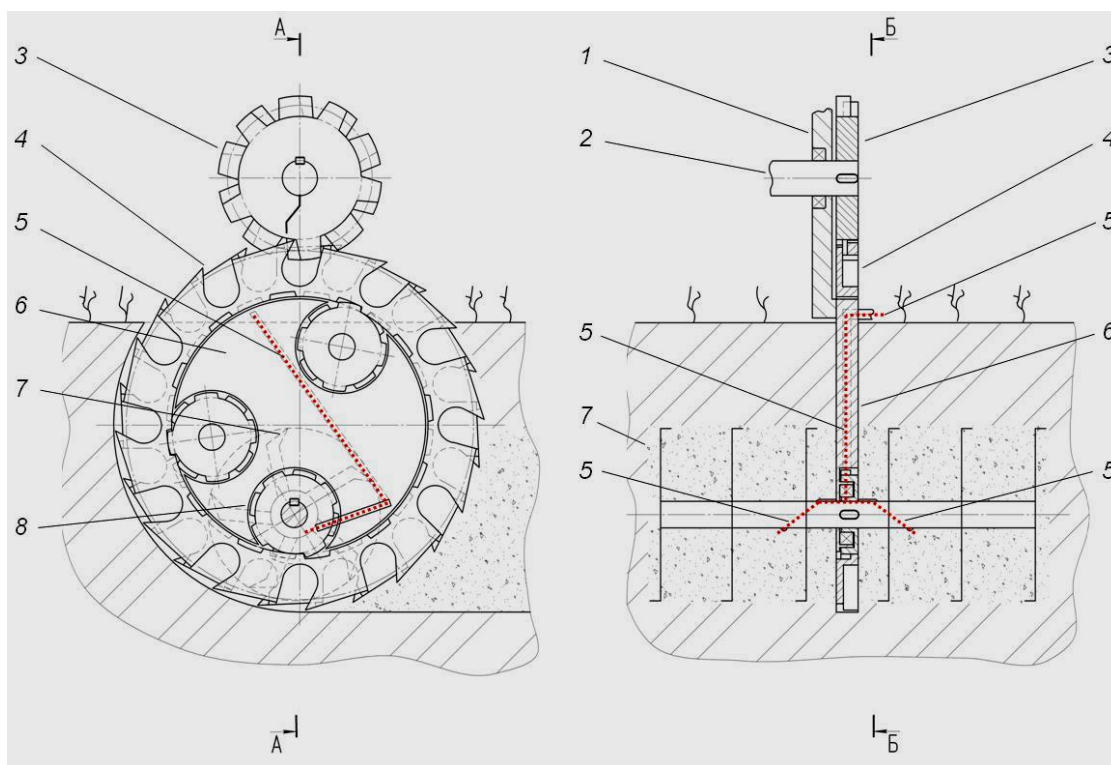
Устройство для внесения вещества в процессе фрезерного внутрипочвенного рыхления
